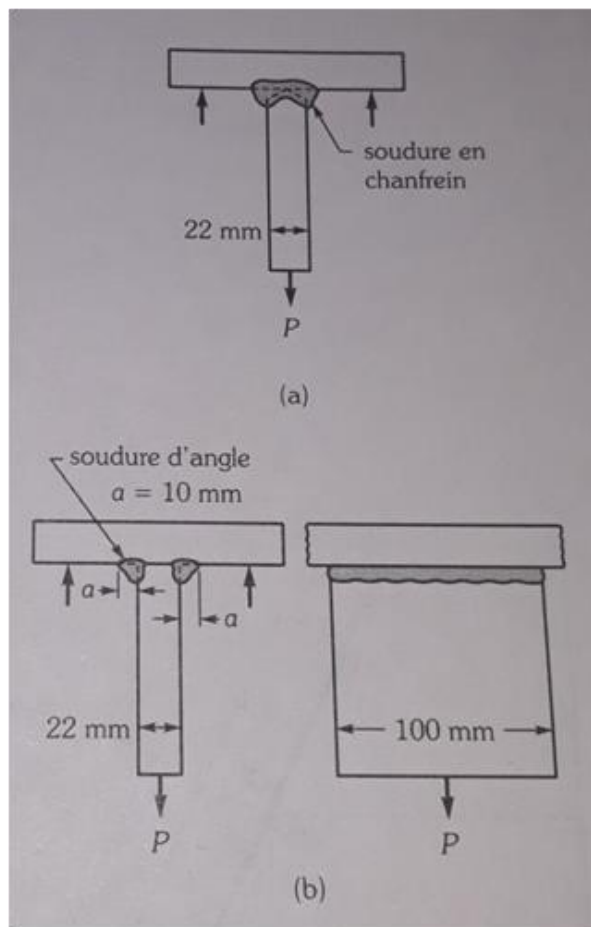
(a) Soudure en chanfrein (b) Soudure d'angle.
